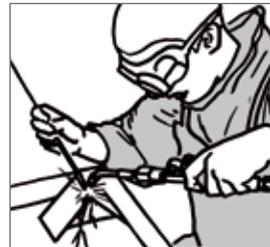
Autogenes Verschweißen zweier Bleche
